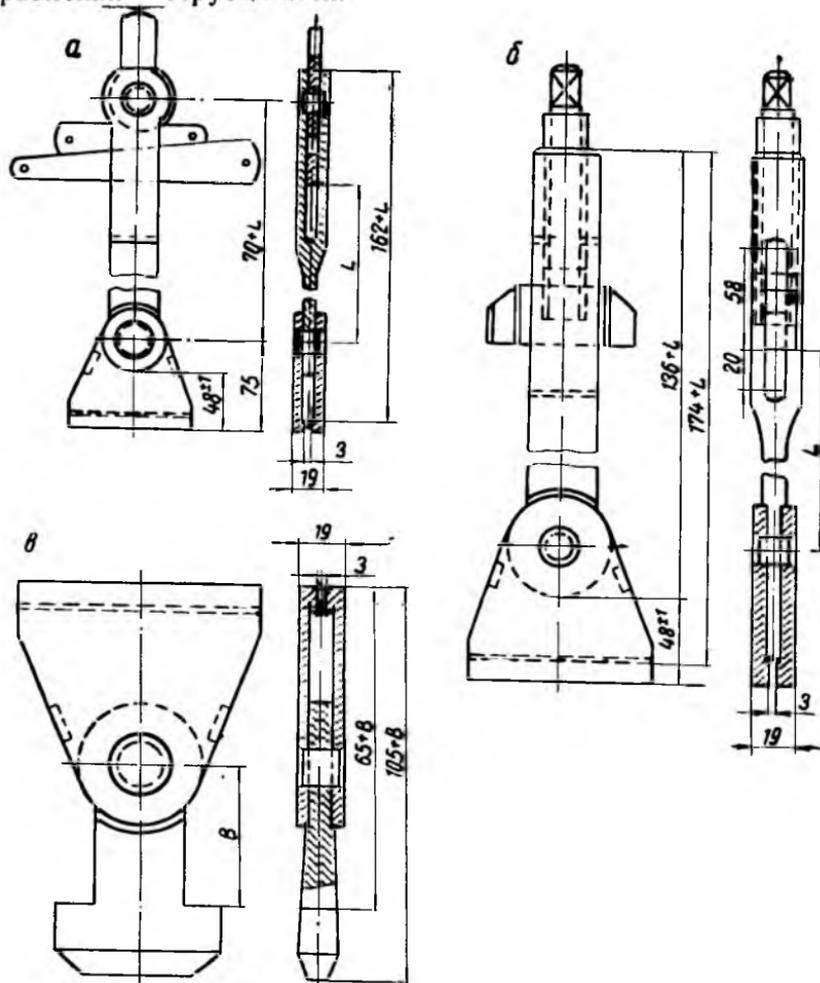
Захваты для укрепления рамных пил в пильной рамке: а — с эксцентриковым натяжным устройством; б — с винтовым натяжным устройством; в — нижний захват
